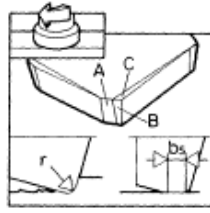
Bir karbür alın freze takım ucu geometrisi
